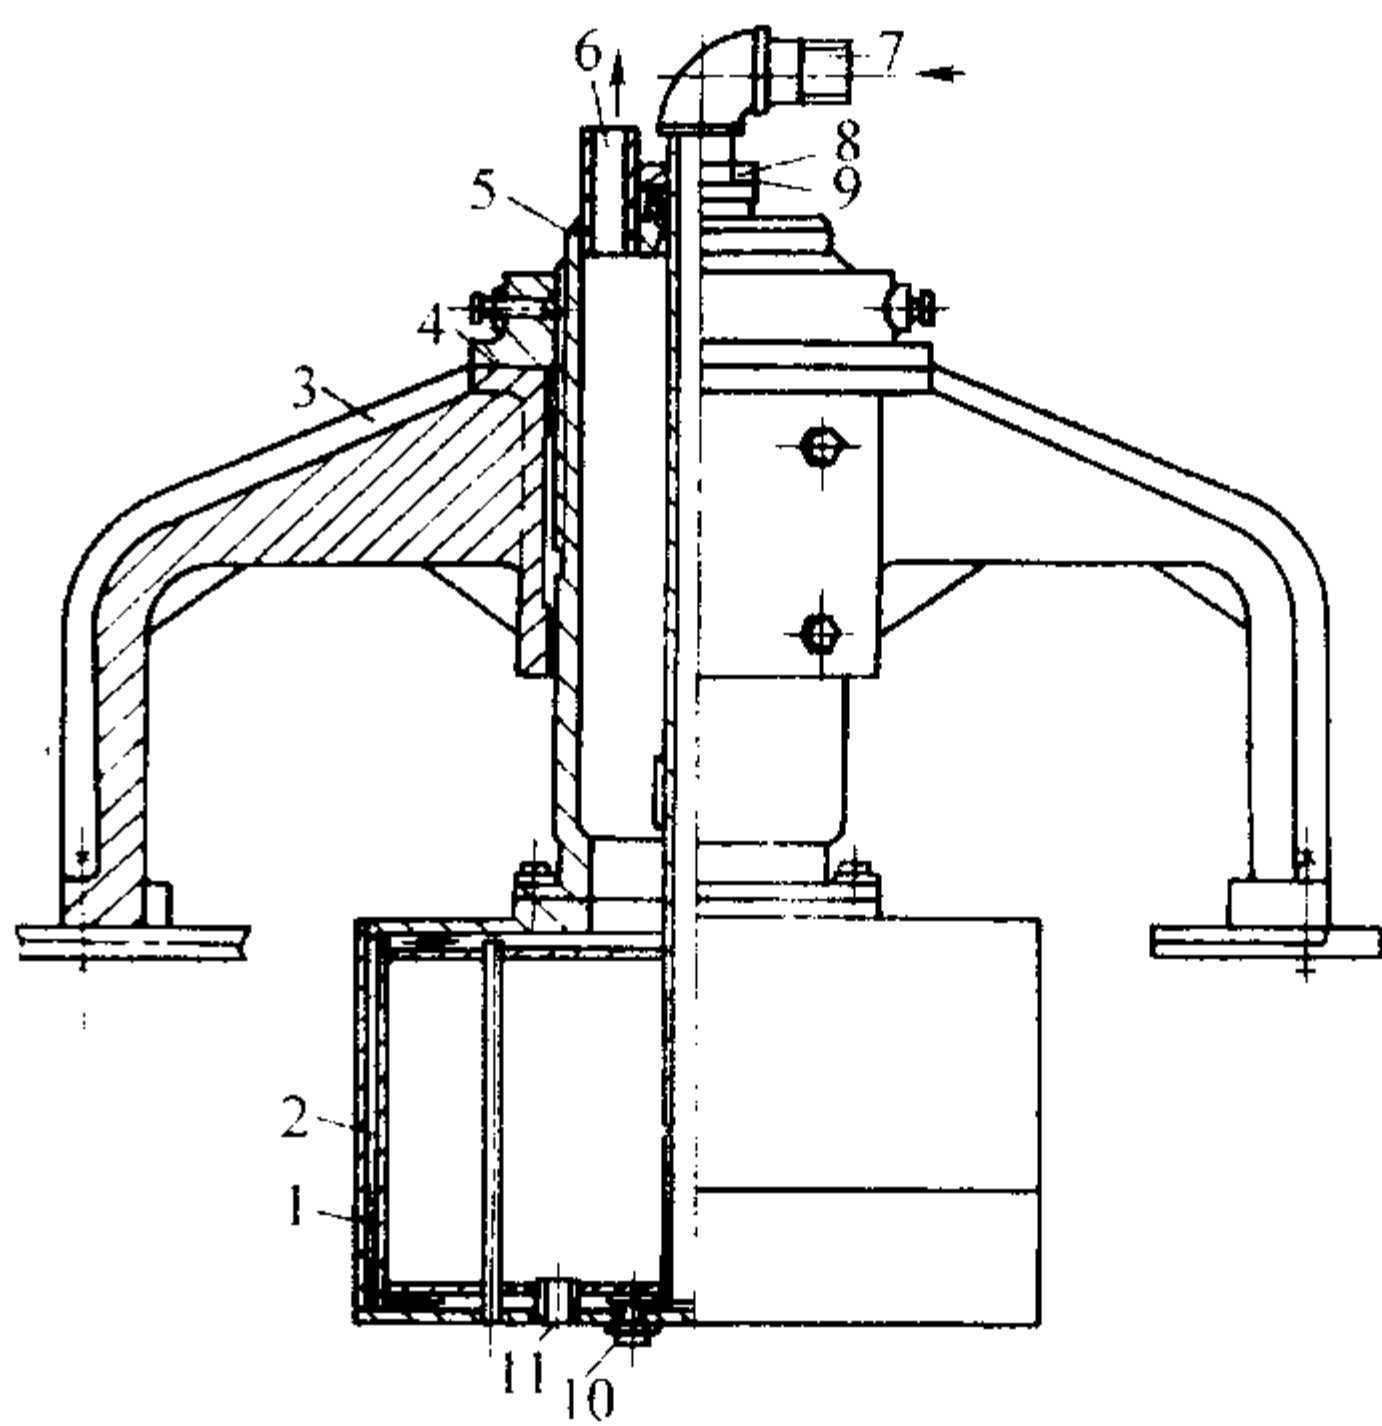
φ1 000 mm 管用焊接钢质内结晶器装配图
